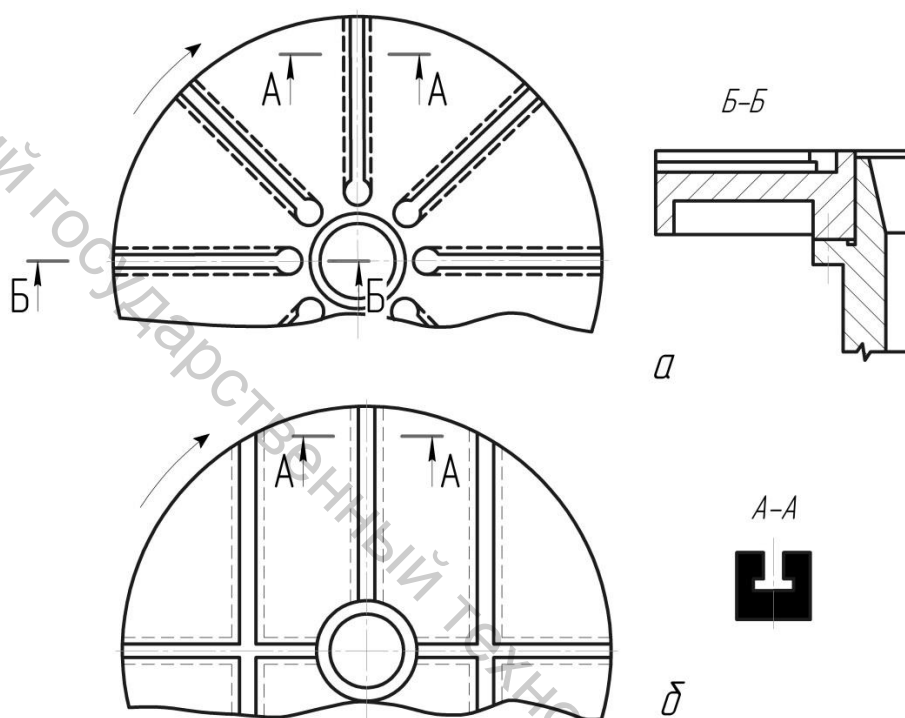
Столы зубофрезерных (а) и карусельнофрезерных (б) станков
